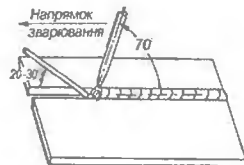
Зварювання тонких листів з подачою присаджувального металу в дугу
